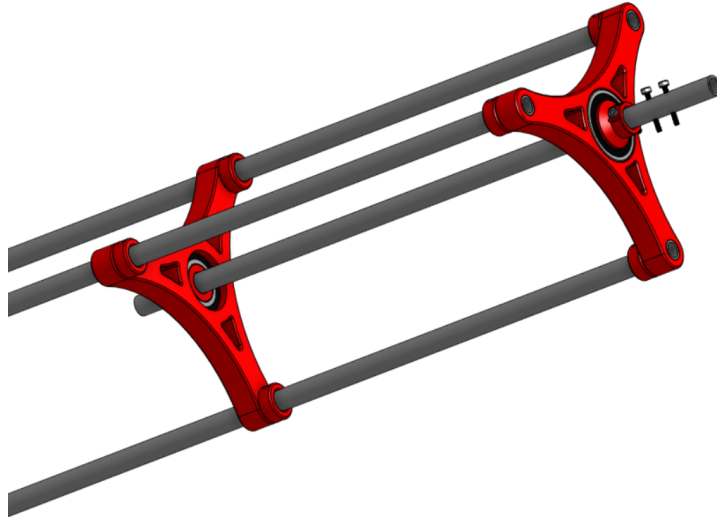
Primer ensamblaje de la estructura principal en Onshape [fuente: elaboración propia]
